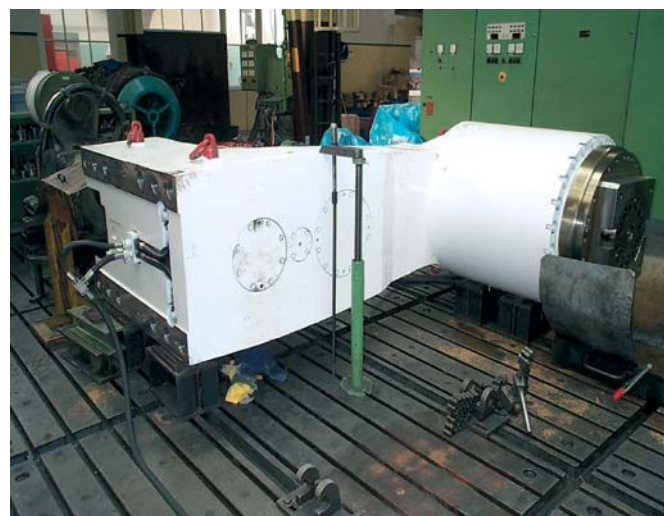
Поворотная рукоять комбайна SL1000 на испытательном стенде
